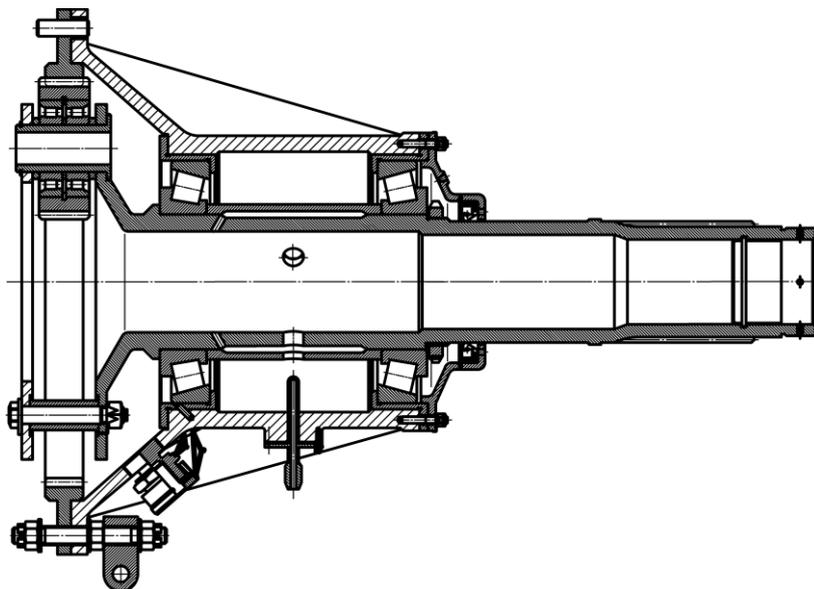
Схема сборки планетарной передачи, выходного вала и корпуса в сборе
